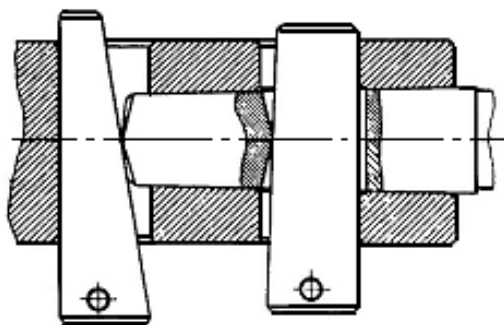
Кріплення інструмента в шпинделі розточувального верстата
